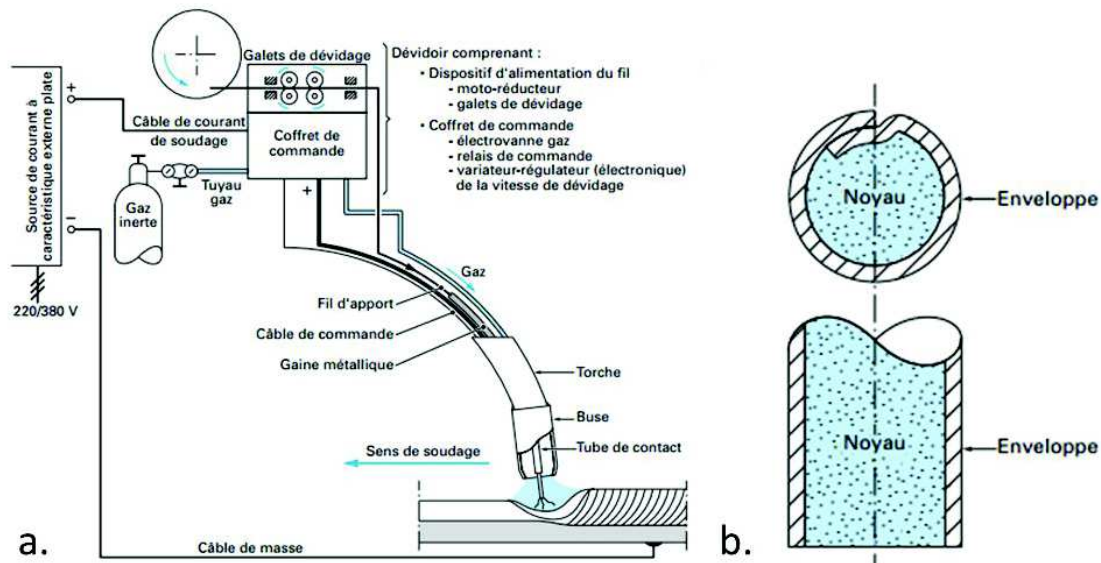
Schéma du procédé de soudage MIG/MAG (a.) et vue de dessus et en coupe du file utilisé pour le procédé FCAW (b.) [Cunat2000]
